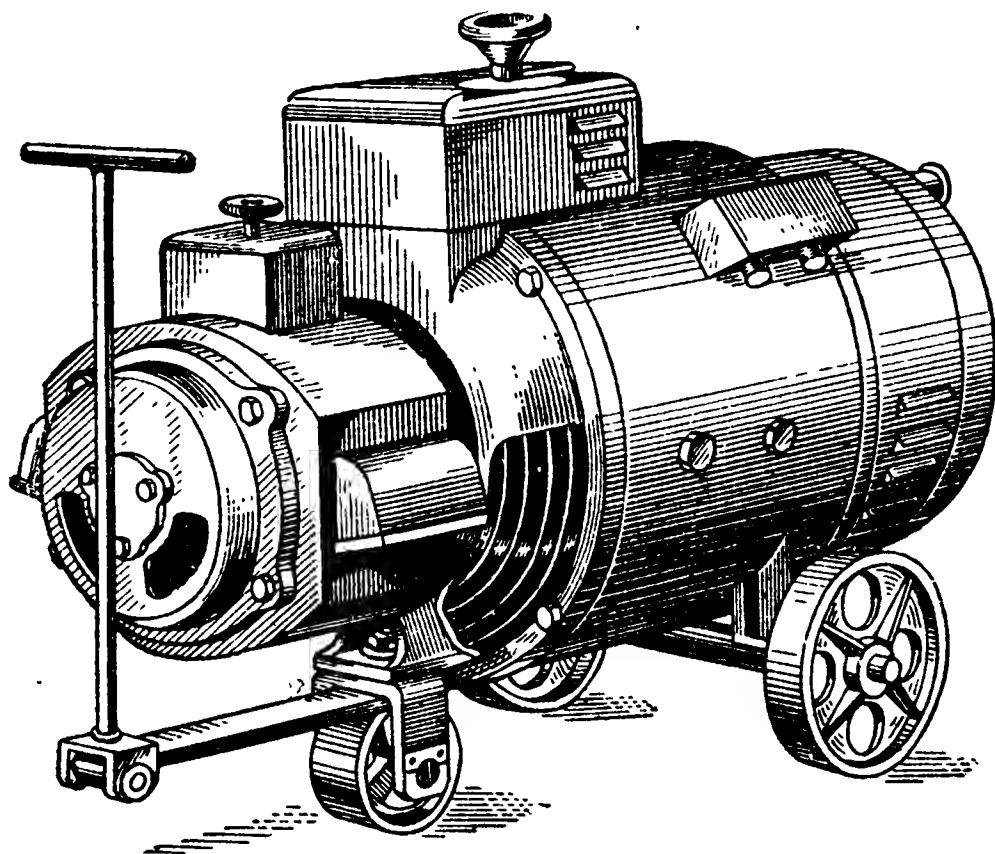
Сварочный агрегат СУГ-2Р-У
